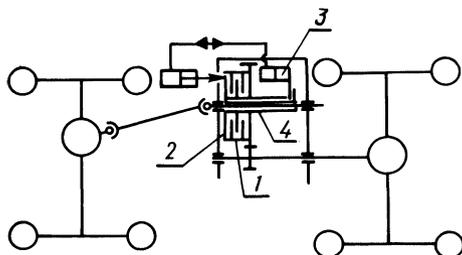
Схема привода ведущих колес трактора с реверсивной фрикционной муфтой.
